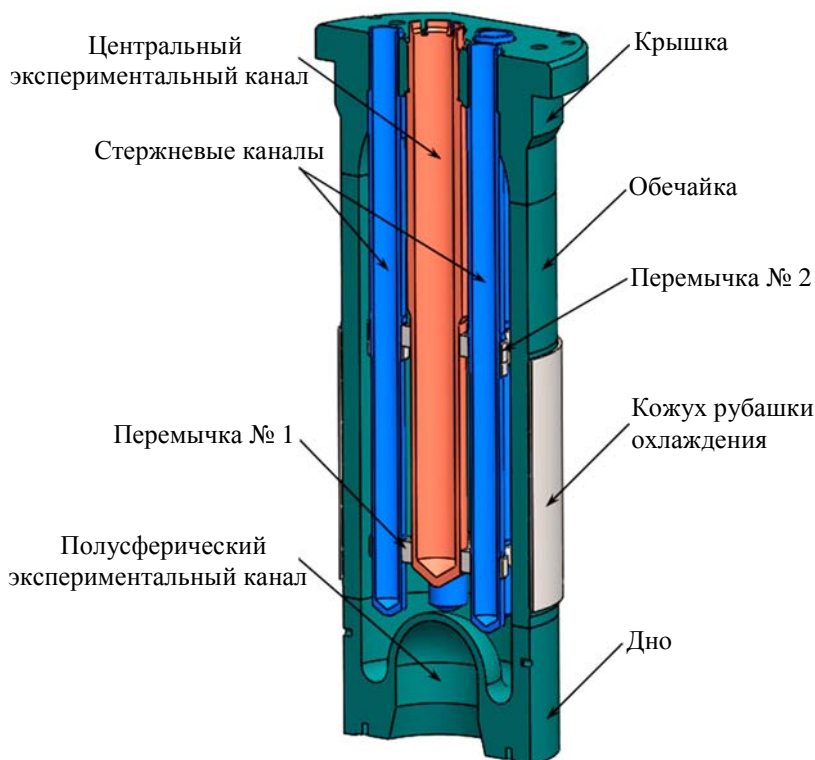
Конструктивная схема корпуса АЗ реактора ВИР-2М
